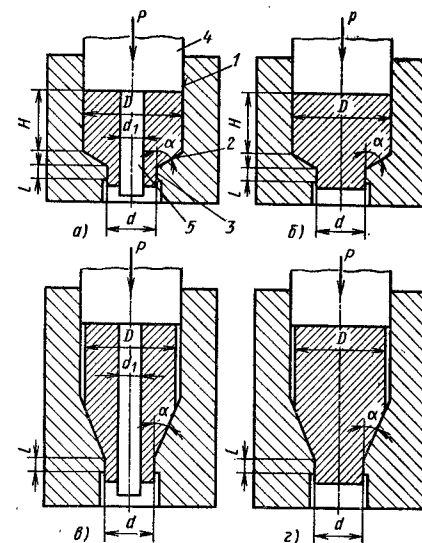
Схемы: а — прямого выдавливания из кольцевой заготовки; б — прямого выдавливания из сплошной заготовки; в — редуцирования и калибровки полых деталей; г — редуцирования и калибровки сплошных деталей; 1 — приемник матрицы; 2 — конический участок матрицы; 3 — цилиндрический пояс матрицы; 4 — наружная ступень пуансона; 5 — центральная ступень пуансона
